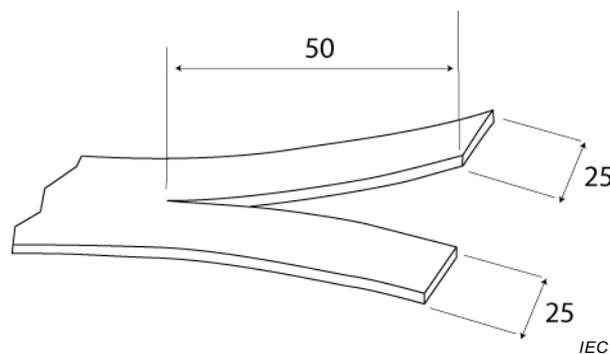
Forme de l'éprouvette pour la résistance à la déchirure
